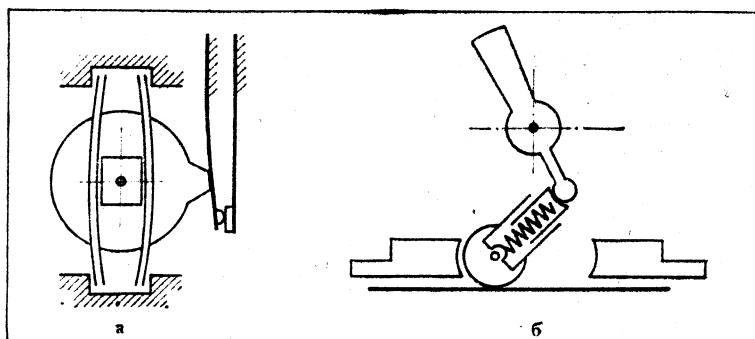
Механизм выключателей (переключателей) кулачкового (а) и тумблерного (б) типа
